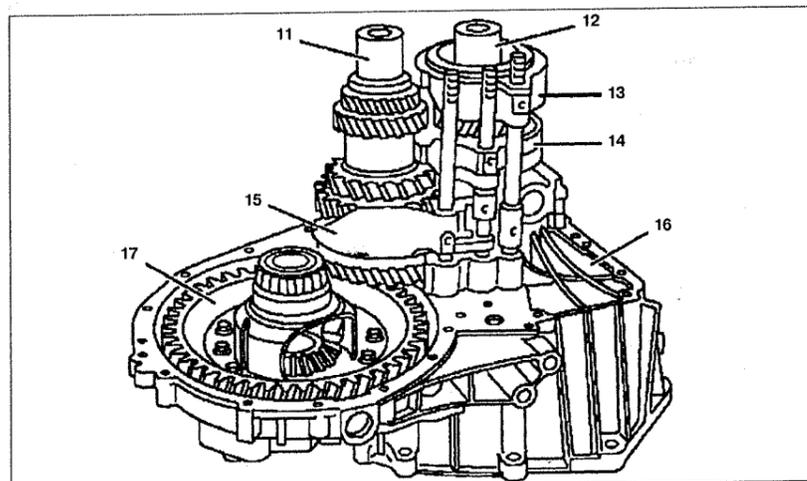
Разборка и сборка коробки передач (автомобили с двигателем 611.980):
